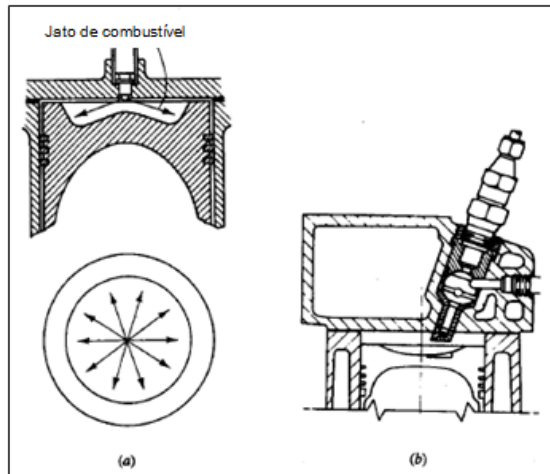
Injeção de combustível em motores diesel: (a) Direta, (b) Indireta.
